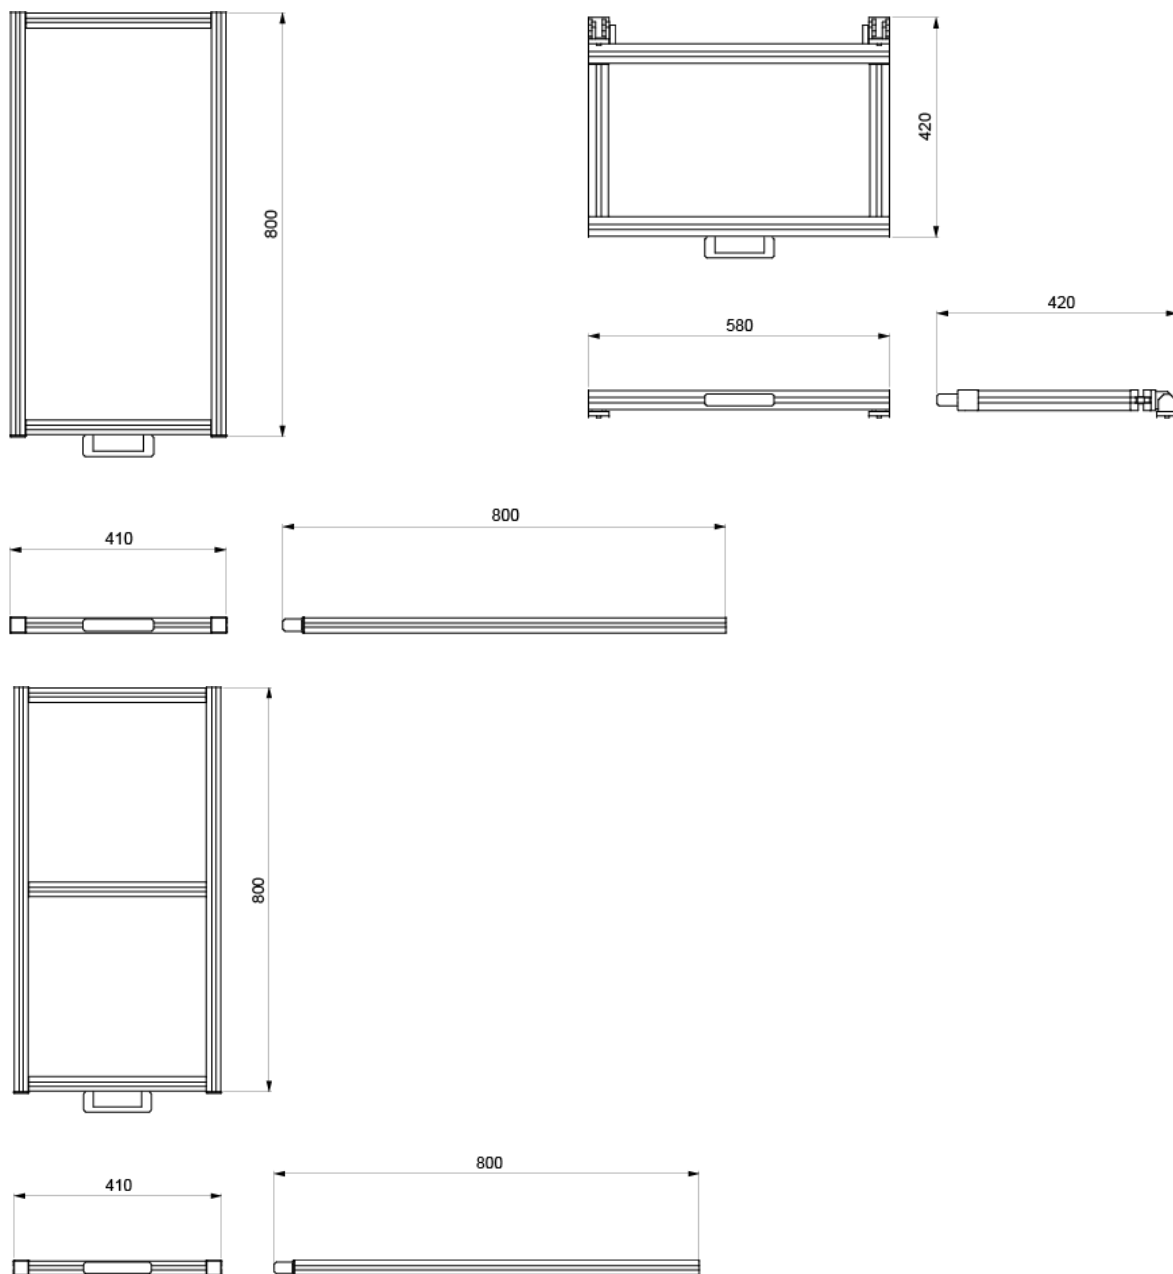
zobrazení půdorysu, nárysu a bokorysu vozíku s nástavbou
